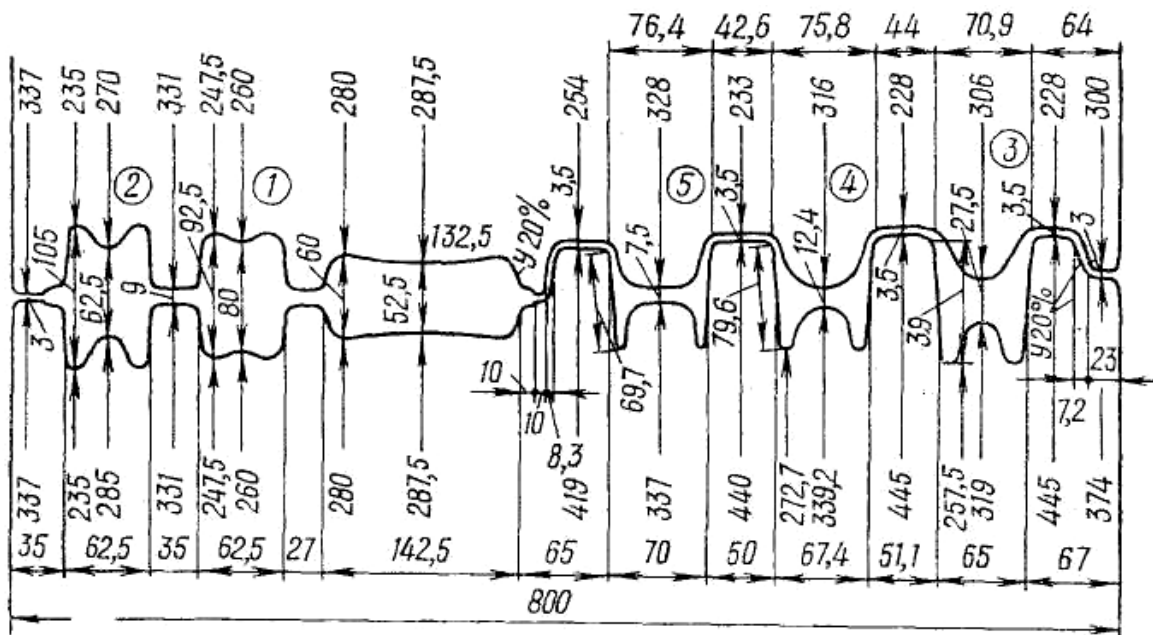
Профіль валків для прокатки заготовки двотаврової балки
